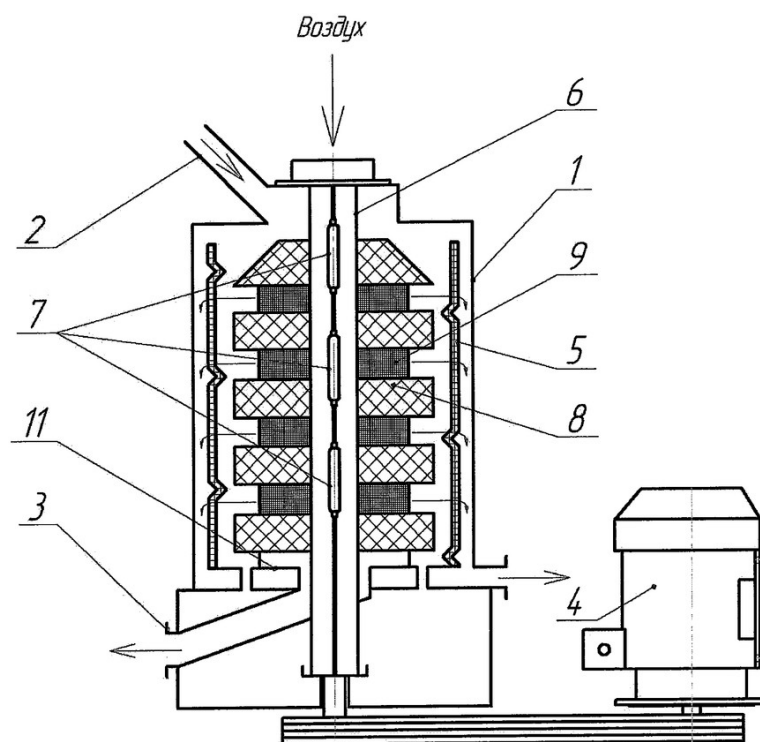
Устройство для шелушения зерна по патенту №2491124
